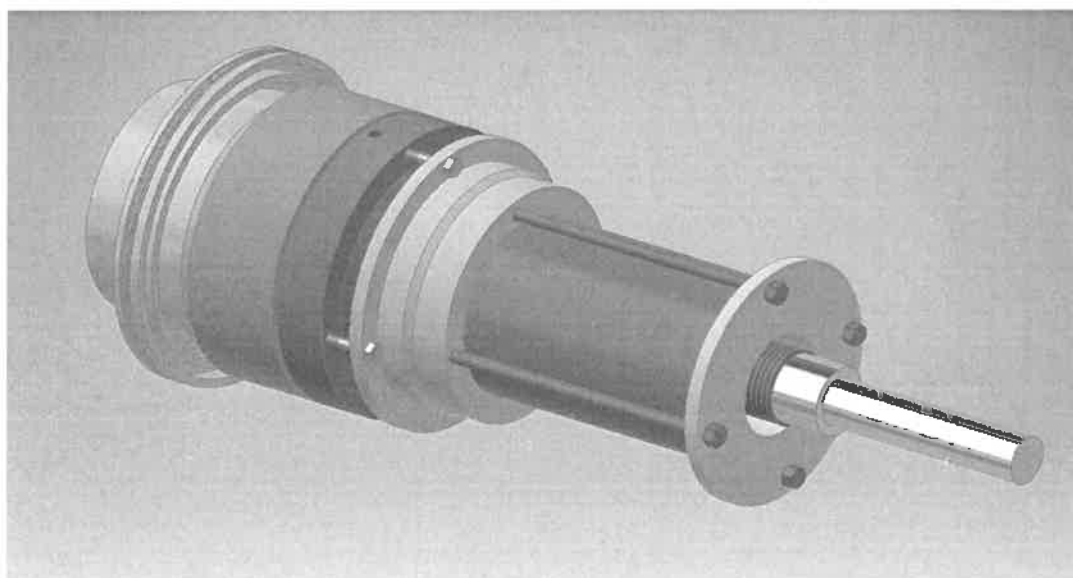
Устройство для демонтажа внутренних колец буксовых подшипников
